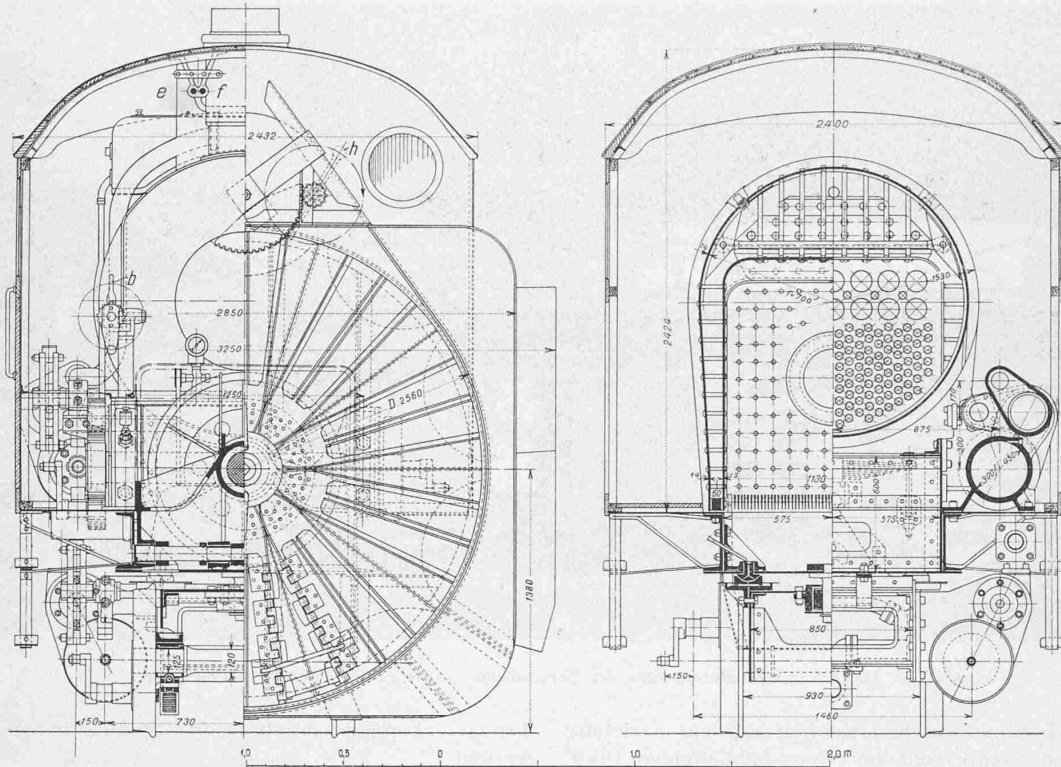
Querschnitte und Frontansicht. — Masstab 1 : 35.
